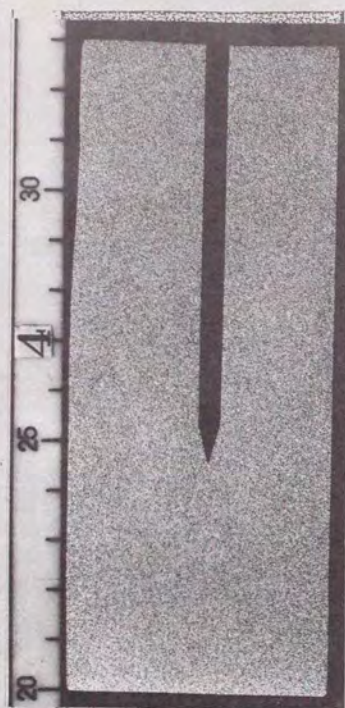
人工欠陥先端部の写真(断面 II-2, II-3)
